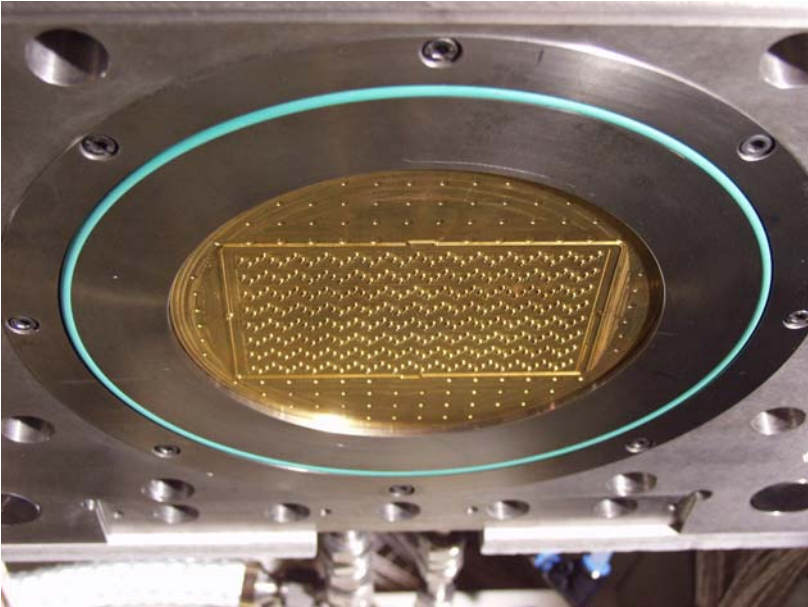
Ansicht der Werkzeugoberhälfte
